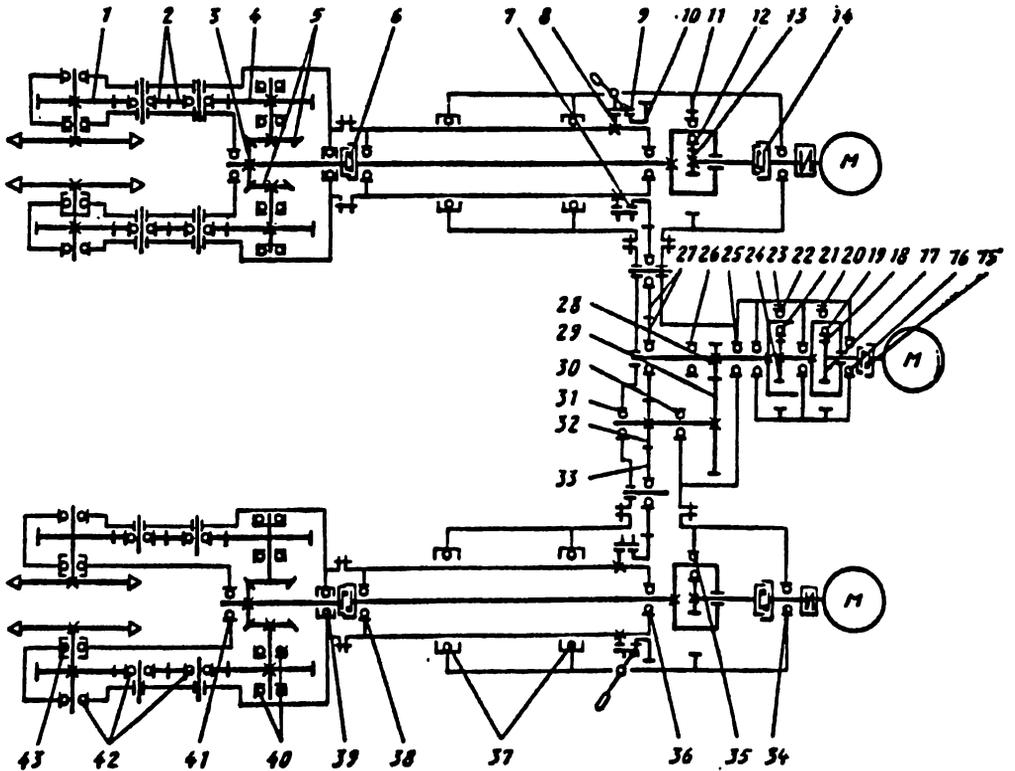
Кинематическая схема привода исполнительного органа комбайна «Урал-10А»:
